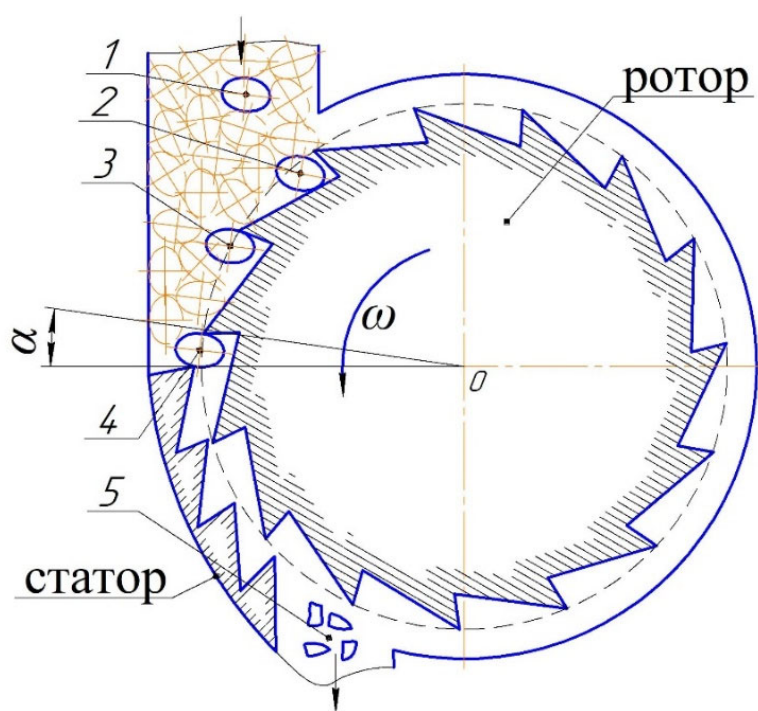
Схема движения зерновки в измельчающей полости горизонтальной роторной дробилки
